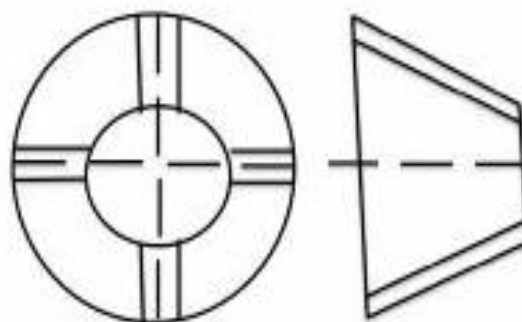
Коническая часть поршня гомогенизатора с направляющими канавками
